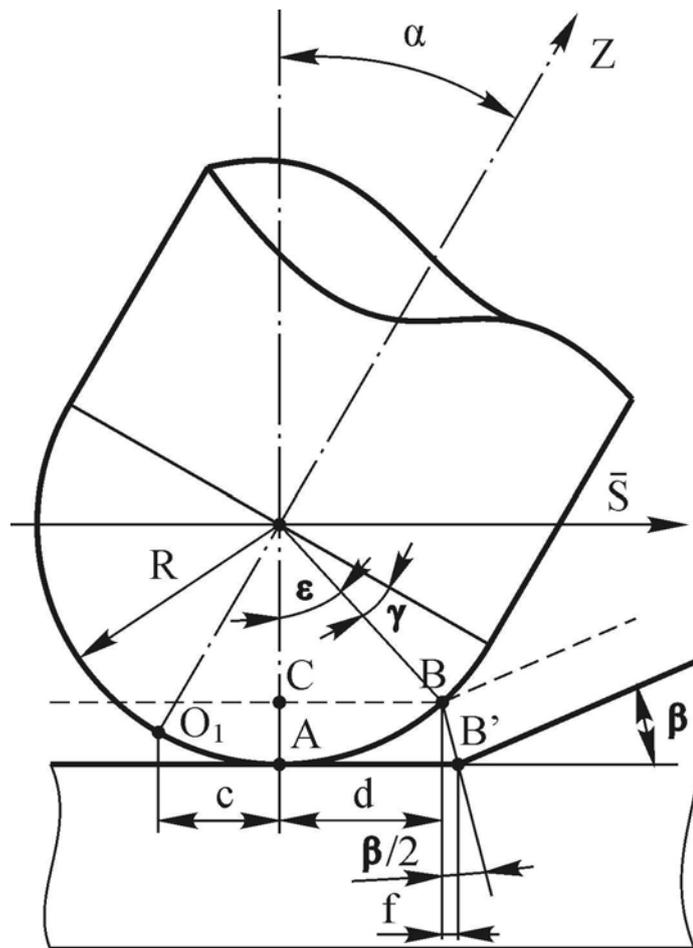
Расчетная схема для определения опорных точек при фрезеровании горизонтального участка детали
